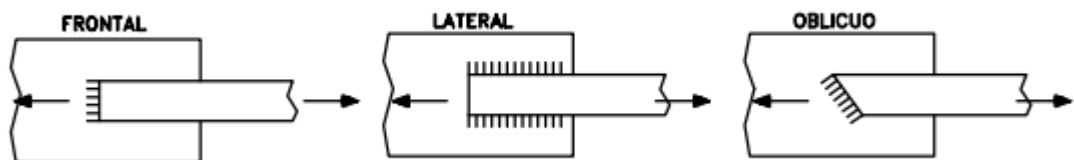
Soldadures segons posició del cordó respecte a l'esforç (Font: Universidad de Castilla la Mancha)
